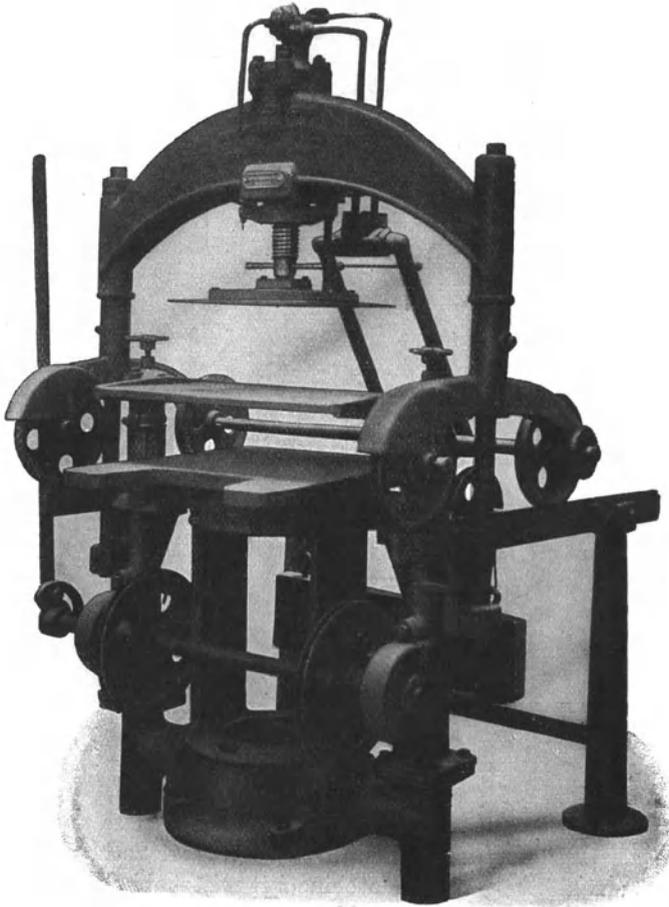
Hydraulische Wendeplatten-Formpresse mit ausfahbarem Preßzylinder (Badische Maschinenfabrik).
